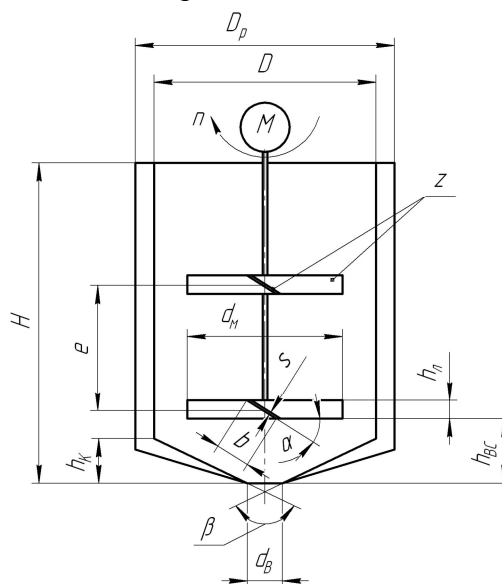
Загальний вигляд реактора естерифікації із лопатевим змішувачем, де: D – діаметр реактора; D_p – діаметр сорочки; H – висота реактора; β – кут при вершині конічного днища; d_m – діаметр змішувача; h_l – висота лопаті змішувача; b – ширина лопаті; α – кут нахилу лопаті змішувача до горизонту; $h_{вс}$ – висота встановлення змішувача; h_k – висота конусної частини реактора; d_B – діаметр зливного патрубку реактора; e – відстань між ярусами лопатей; z – кількість лопатей на одному ярусі; V_p – об'єм реактора; n – частота обертання вала змішувача
